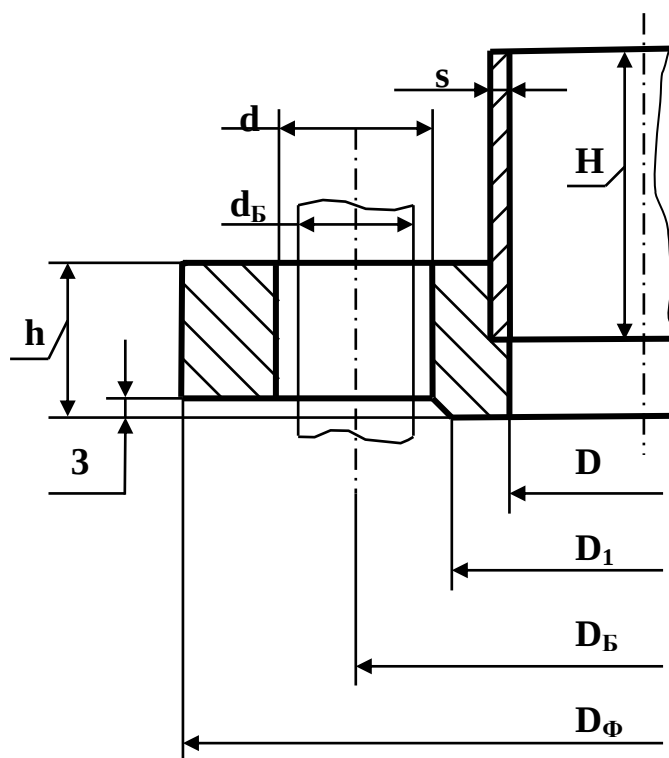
Фланец корпуса и рубашки аппарата
